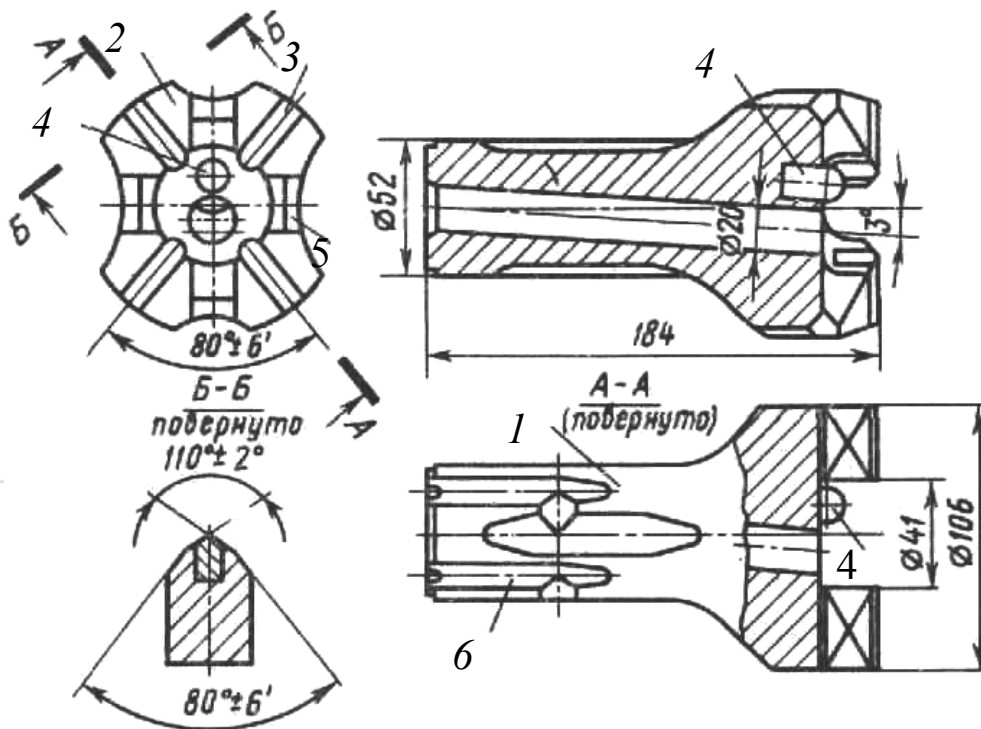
Буровая коронка К-105К для пневмоударника
